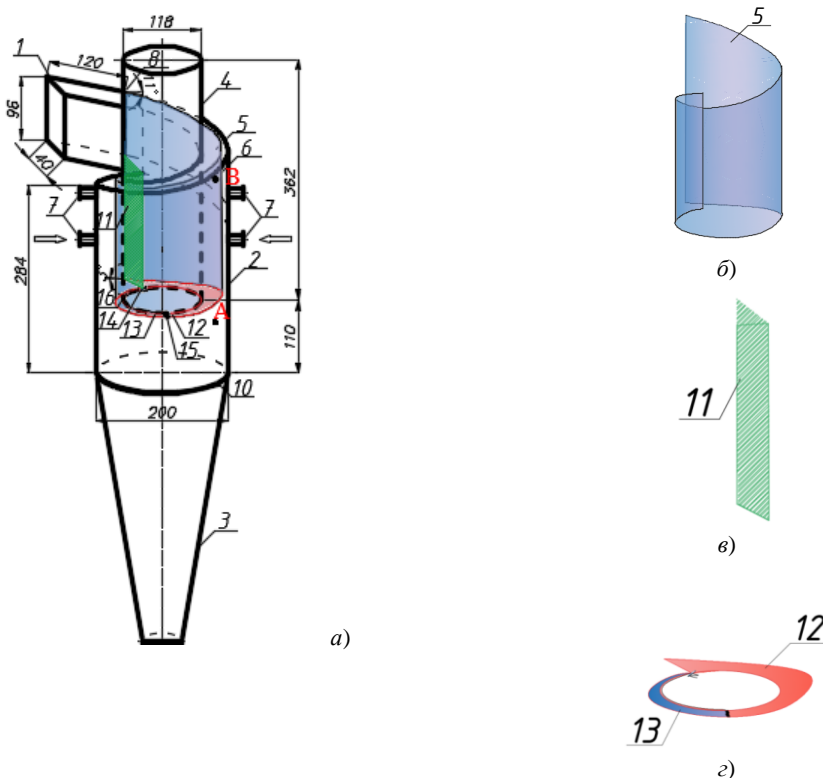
Схема конструкции циклона-фильтра: *1* – входной патрубок; *2* – цилиндрический корпус; *3* – коническое днище; *4* – выхлопная труба; *5* (*б*) – фильтровальный материал; *6* – металлический каркас; *7* – продувочные штуцера; *8* – торец циклона; *9* – заслонка; *10* – детали крепежа; *11* (*в*) – поперечный фильтр; *12* (*з*) – горизонтальный фильтр, тканая часть; *13* – горизонтальный фильтр, металлическая часть; *14* – пластина с пружиной; *15* – стержень с кольцами; *16* – складывающийся фильтр; *A, B* – порты ввода термоанометра
